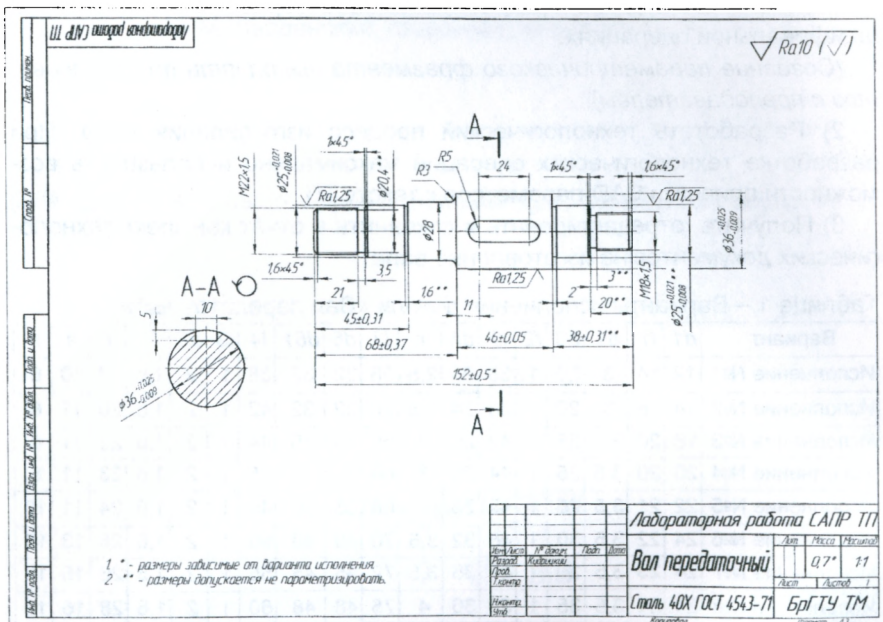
Рабочий чертёж детали «Вал передаточный»
